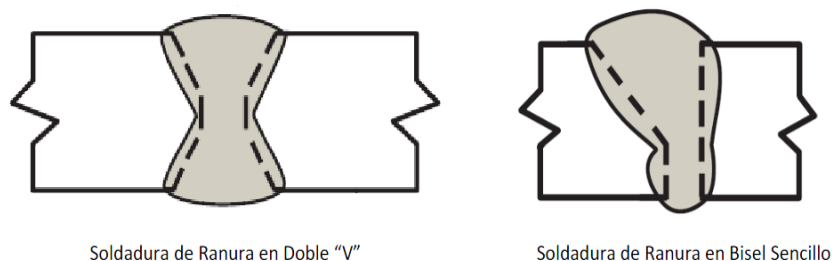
Tipos de soldaduras (doble V y Bisel sencillo).
